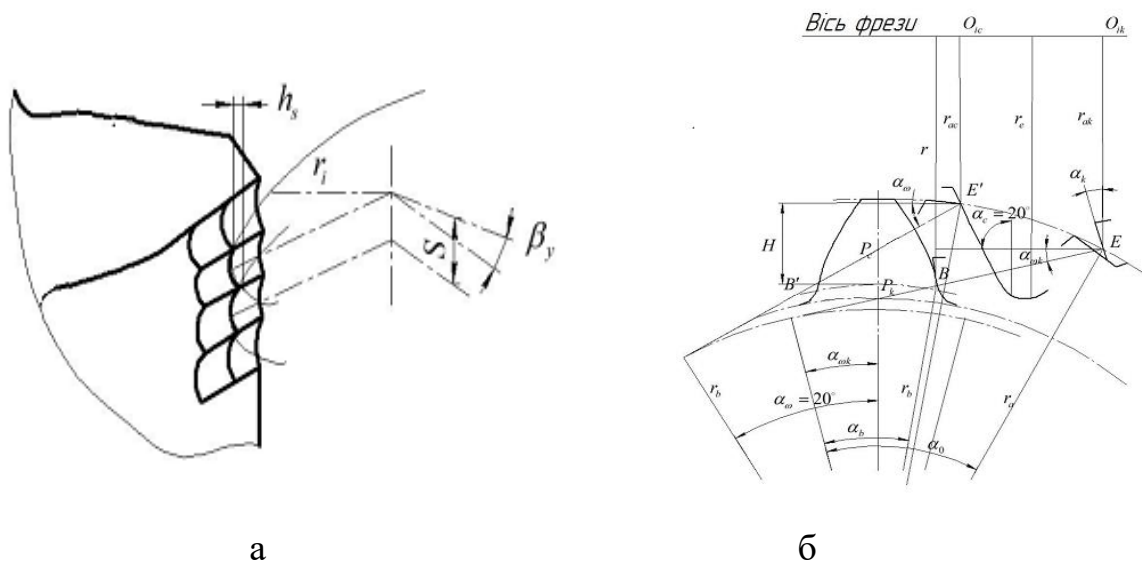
Визначення розрахункової (геометричної) величини хвилястості обробленої поверхні: а - схема утворення хвилі на бічній поверхні зуба колеса; б - визначення розміру радіусів обертання точок зубів фрези, що формують хвилю біля вершини зуба колеса
